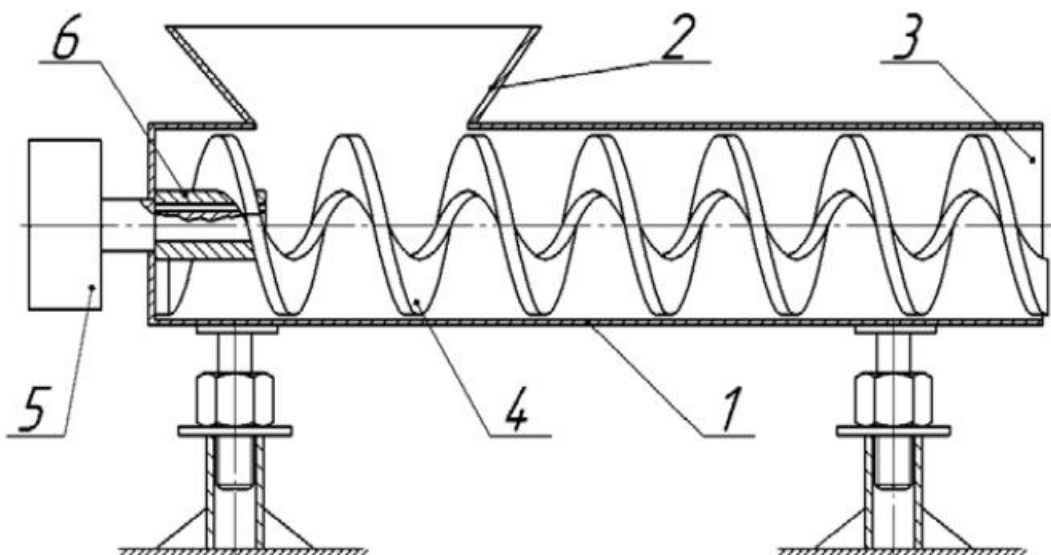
Принципова схема спірально-гвинтового дозатора 1 – циліндричний корпус; 2 – завантажувальна горловина; 3 – розвантажувальна горловина; 4 – спіраль; 5 – привод (мотор редуктор); 6 – муфта.
